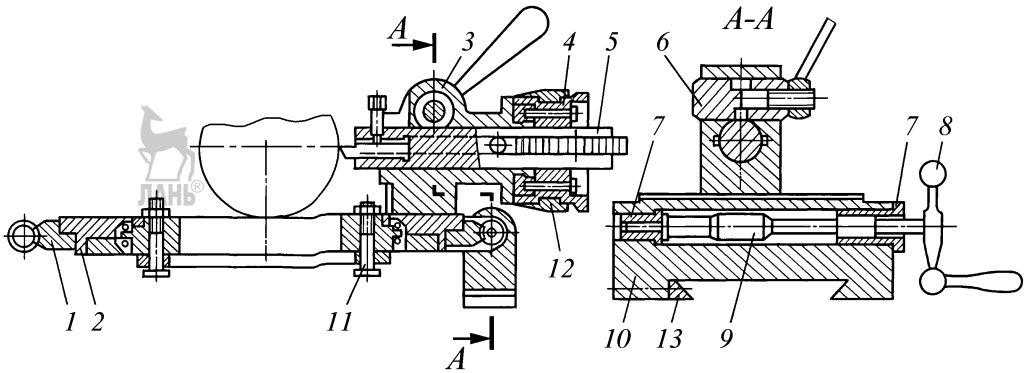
Приспособление для расточки сферических поверхностей:
